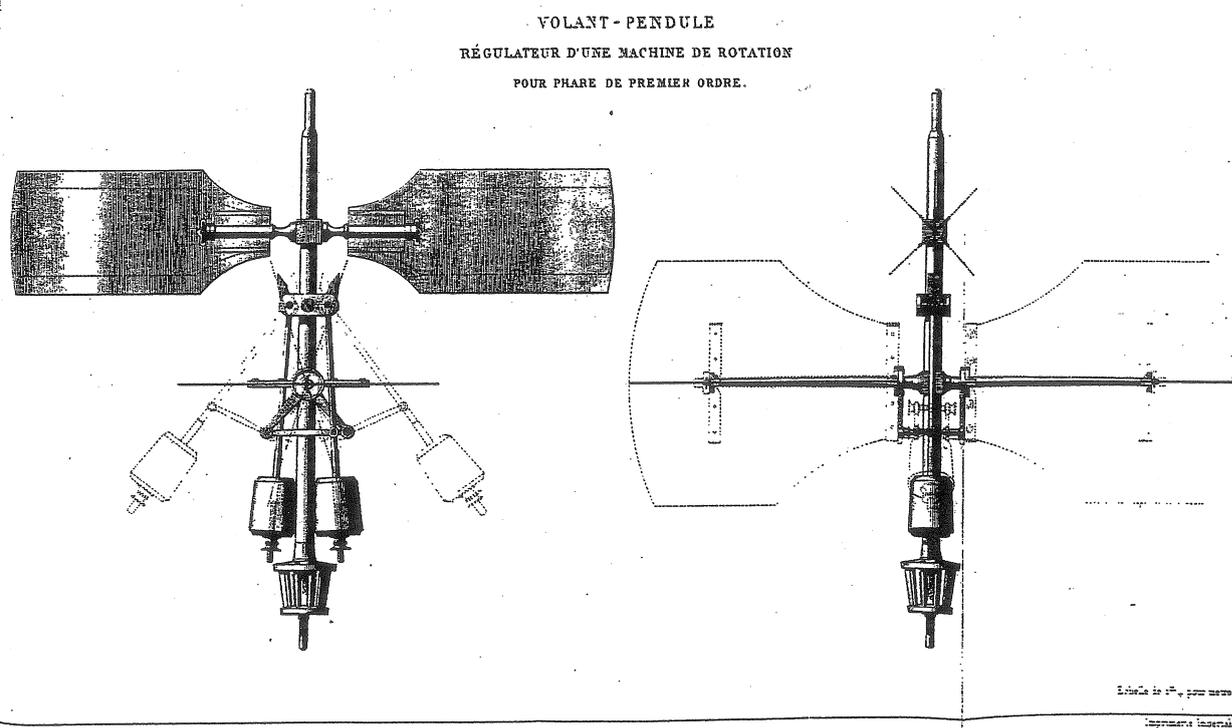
Volant-pendule régulateur pour une machine de rotation.
